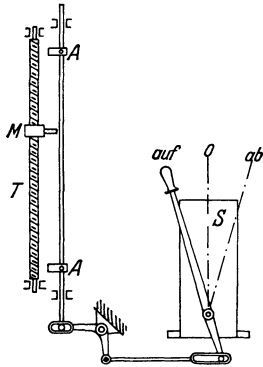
Mechanische Ausrückung bei einer Fördermaschine.
